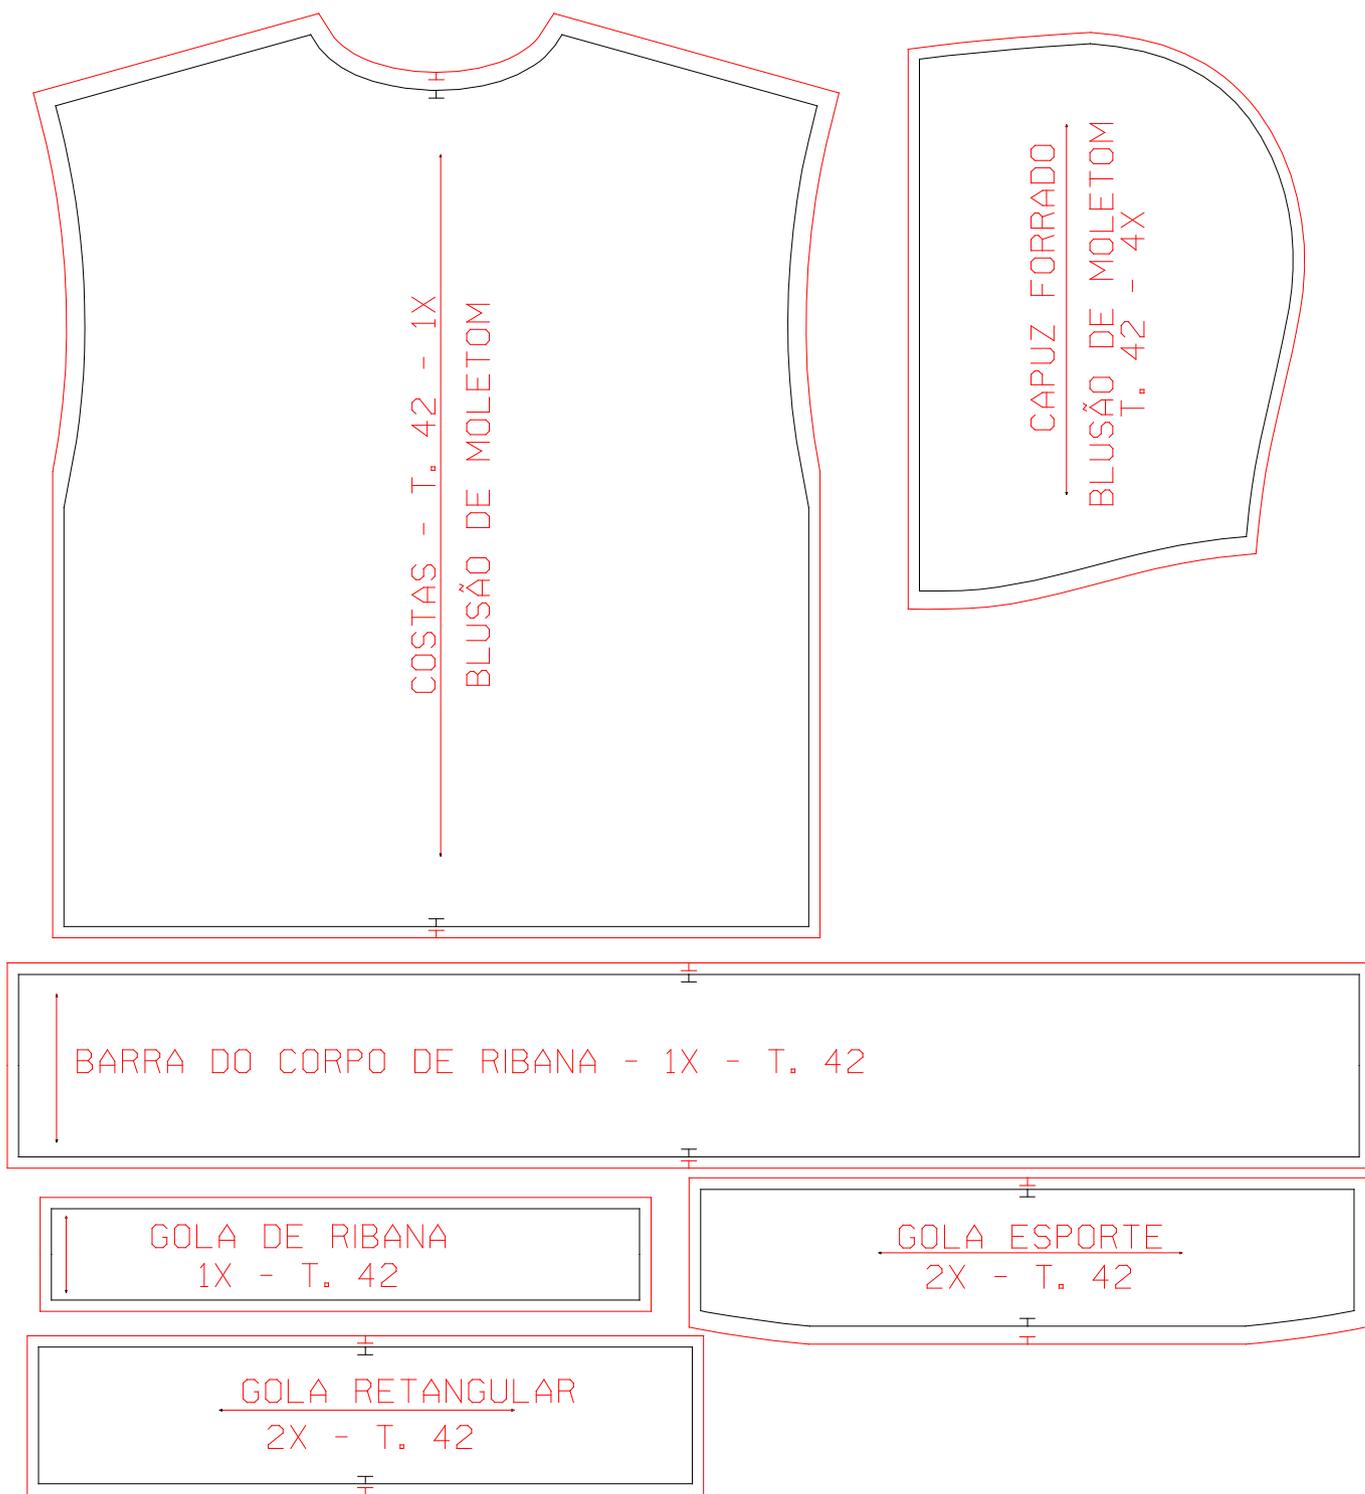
Molde Blusão de Moletom com Zíper (Parte 2) – Escala 1:5
